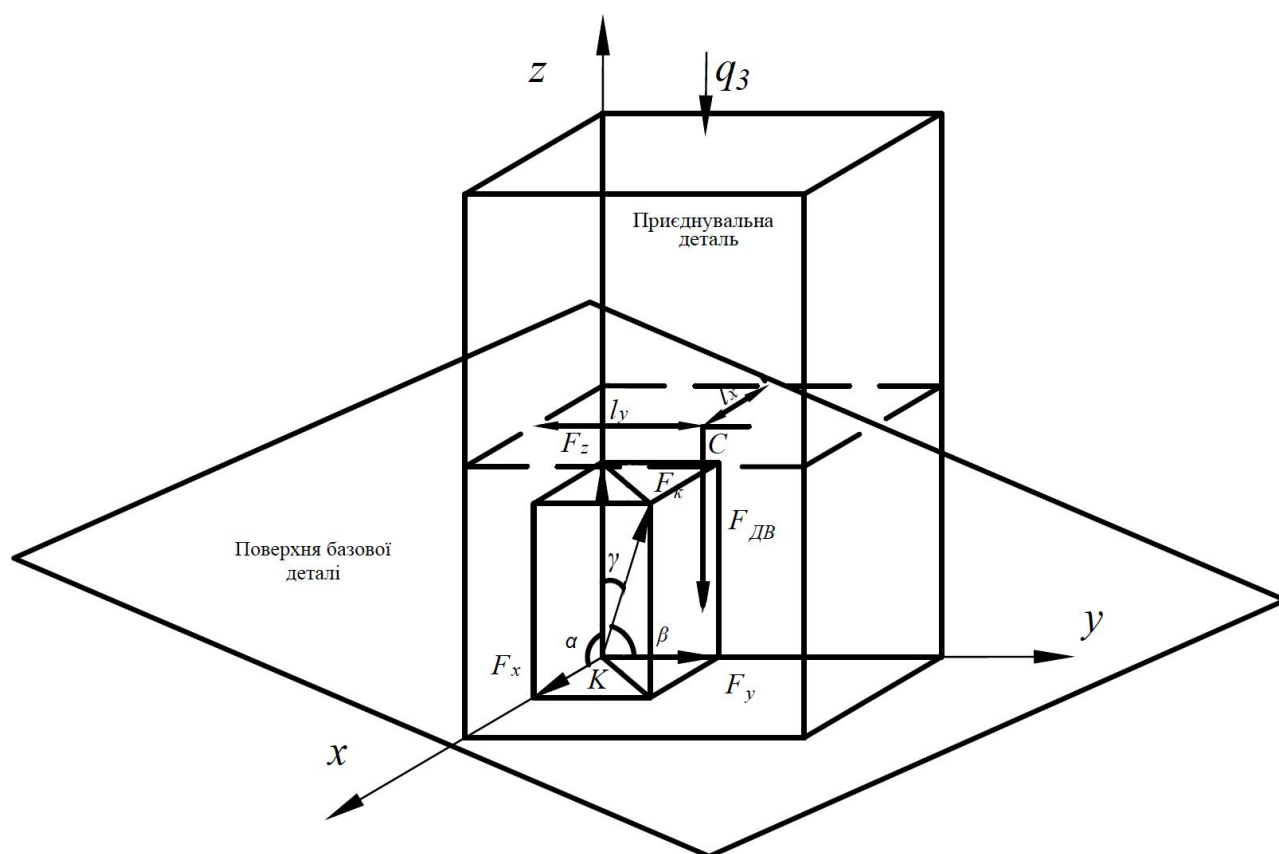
Схема сил, що діють на приєднувану деталь при контакті з поверхнею базової деталі
